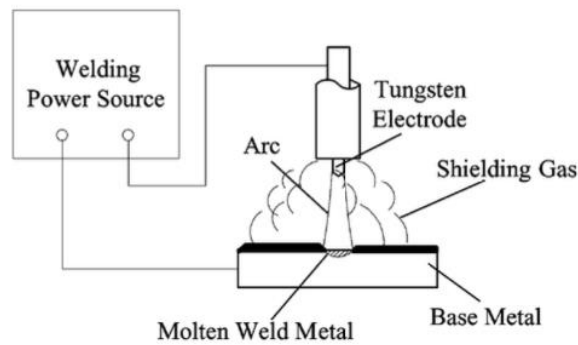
Diagrama del proceso de soldadura TIG.
